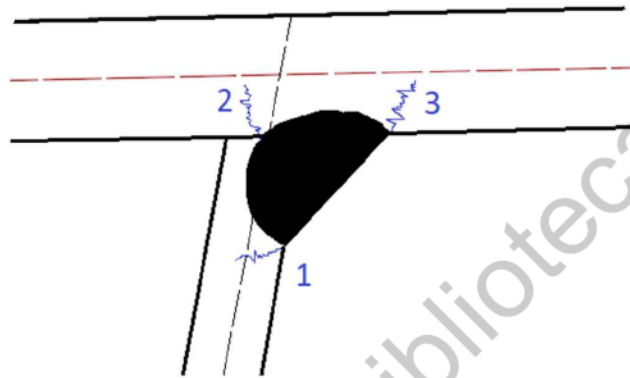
Puntos susceptibles de inicio de grieta en soldadura artesana-placa
